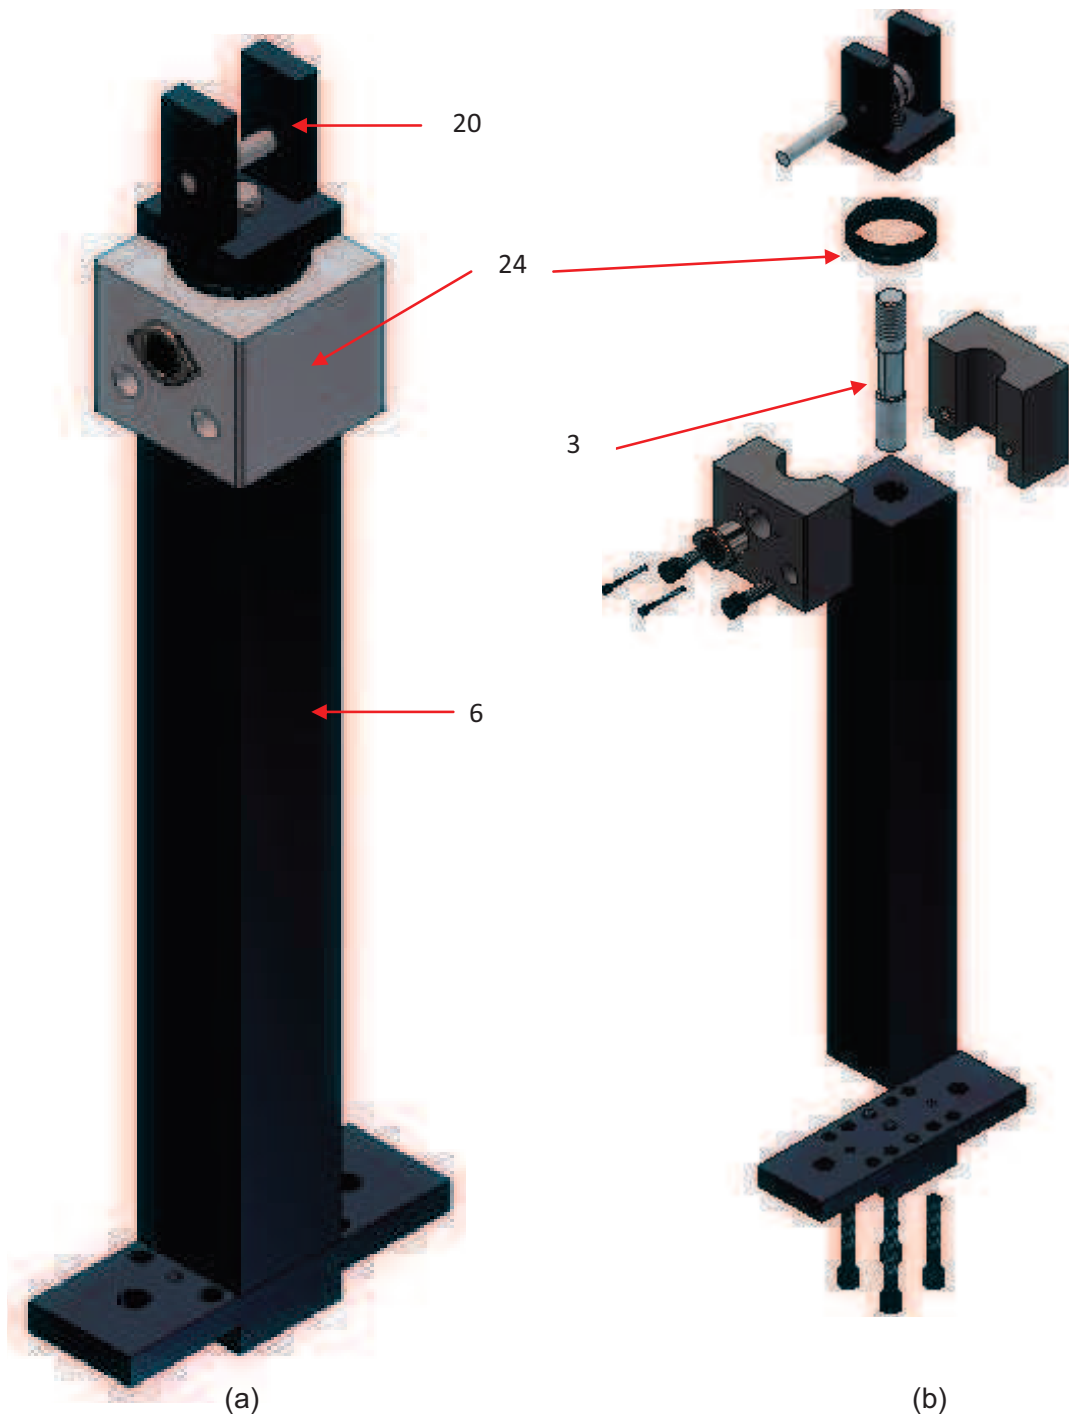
(a) Ensamble de los componentes de la columna instrumentada, (b) Explosivo de la columna instrumentada.
